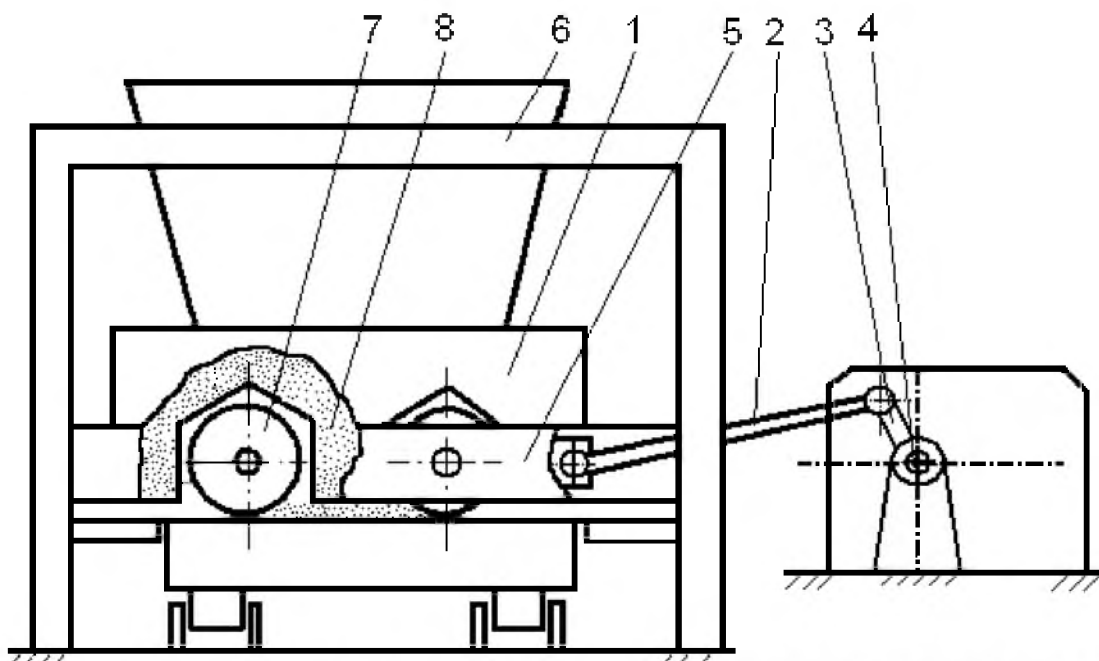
Роликова формувальна установка з кривошипно-повзунним приводом зворотно-поступального руху формувального візка
